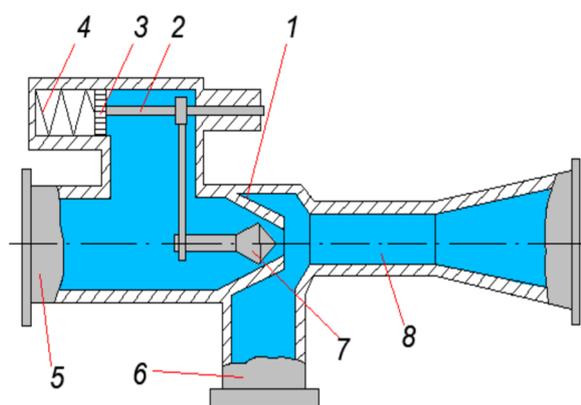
Саморегулируемый игольчатый струйный насос: 1 - сопло; 2 – подвижная ось; 3 - поршень; 4 - пружина; 5 - напорная труба; 6 - всасывающая труба; 7 - игла; 8 - смесительная камера.
